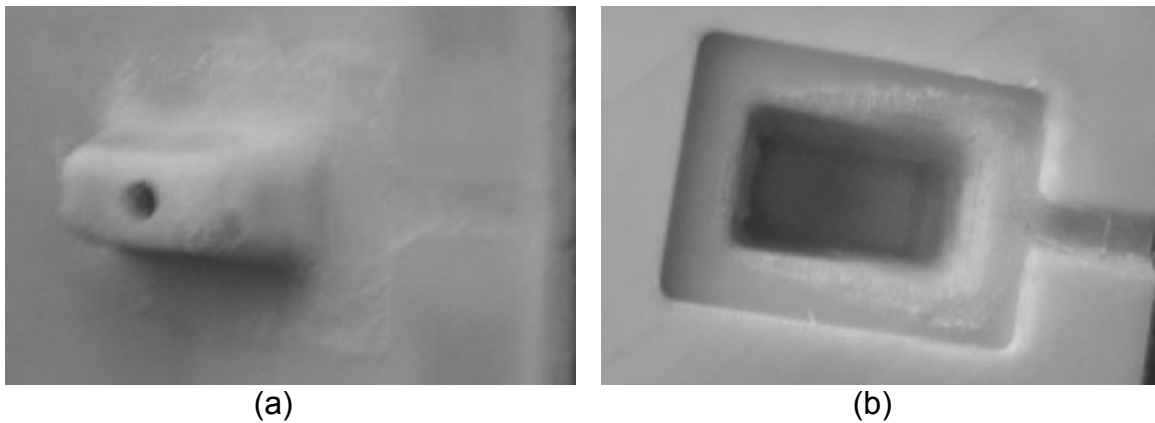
Aspecto da superfície dos inserts após a injeção de 18 peças de PA:
